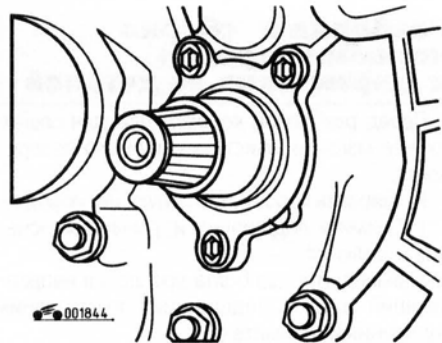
Установка направляющей втулки подшипника выключения сцепления
